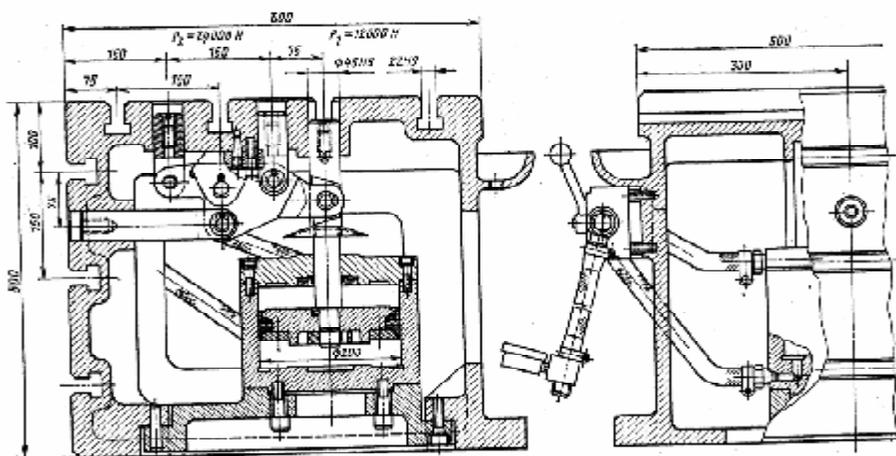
49 – Стол - тумба неподвижный с пневмоприводом
